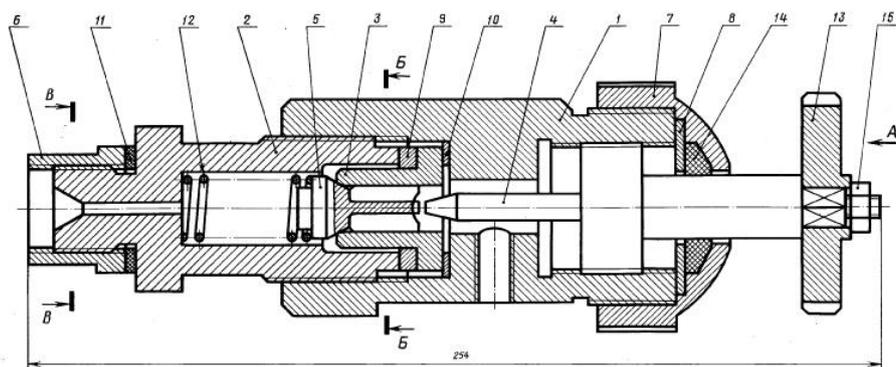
Чертеж выключателя подачи топлива дизеля, где цифрой 1 обозначен корпус
